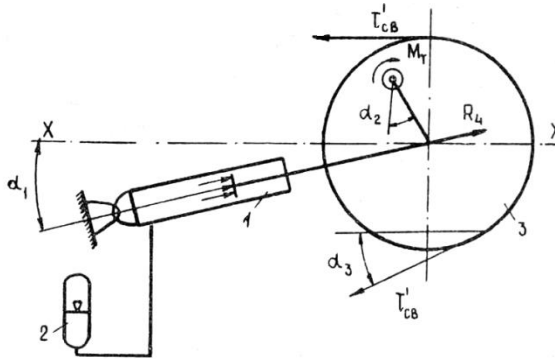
Схема пристрою автоматичного підтримування натягу направляючого колеса: 1—гідроциліндр; 2 – гідропневматичний акумулятор; 3 – натяжне колесо
